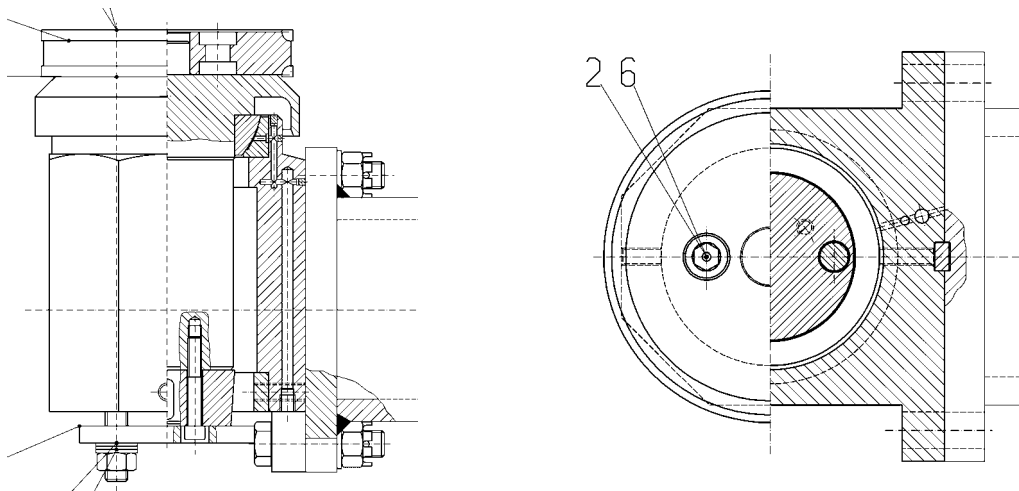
(a) Vista lateral da Lâmina com suporte; (b) Vista superior da Lâmina com suporte.
